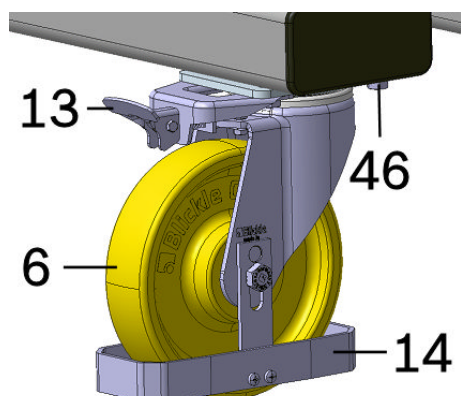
Сменное самоустанавливающееся колесо, детальный вид
